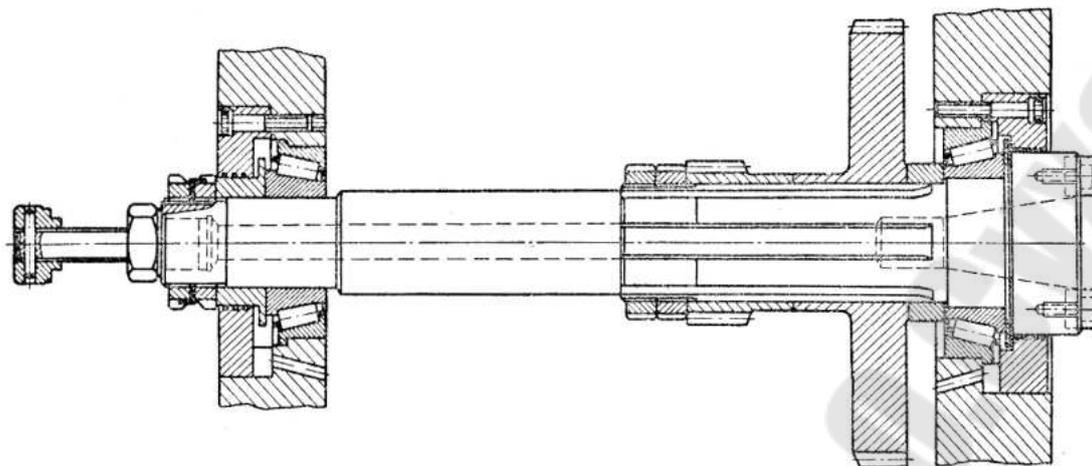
Шпиндельный узел легкого фрезерного станка
